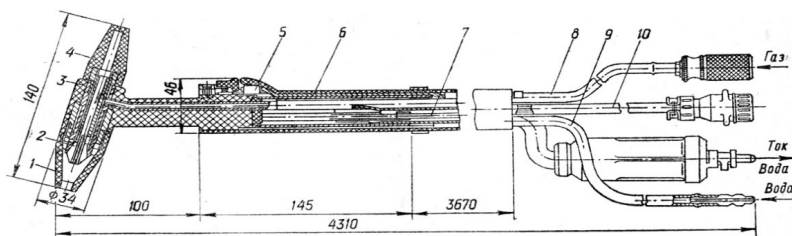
Пальник для ручного зварювання типу ГР
